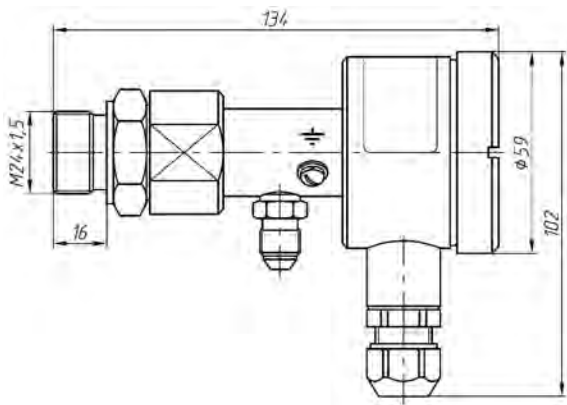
Внешний вид и устройство блоков датчика преобразователей МТМ701.5П-ОМ-П-01
